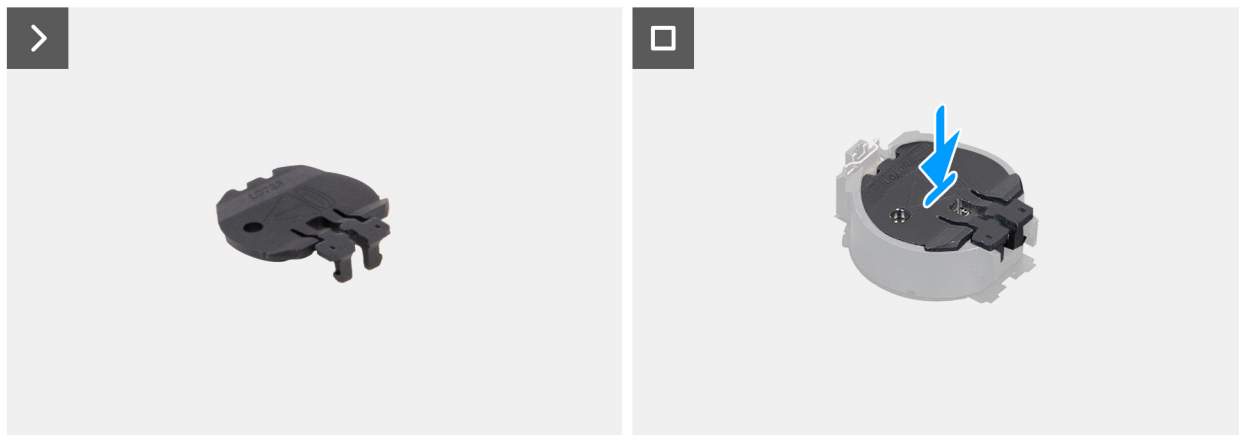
Instalación de la cubierta de la batería de tipo botón
